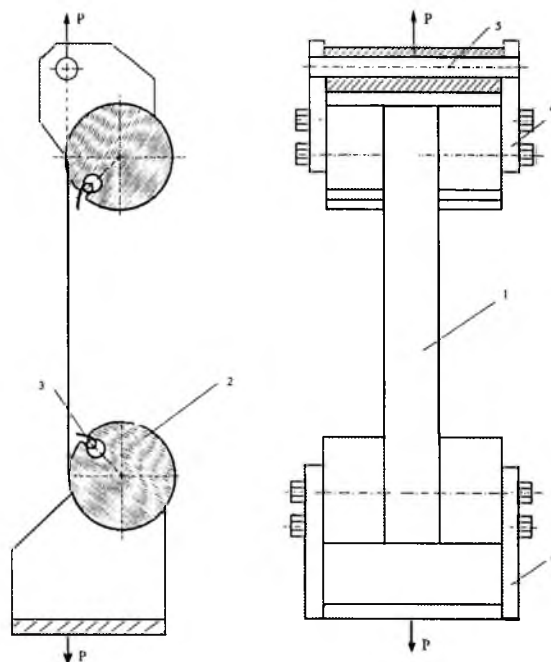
Устройство для закрепления ленты при испытании на разрыв: 1 – лента; 2 – барабан улитки; 3 – клин; 4 – пластины; 5 – ось нагружения.
